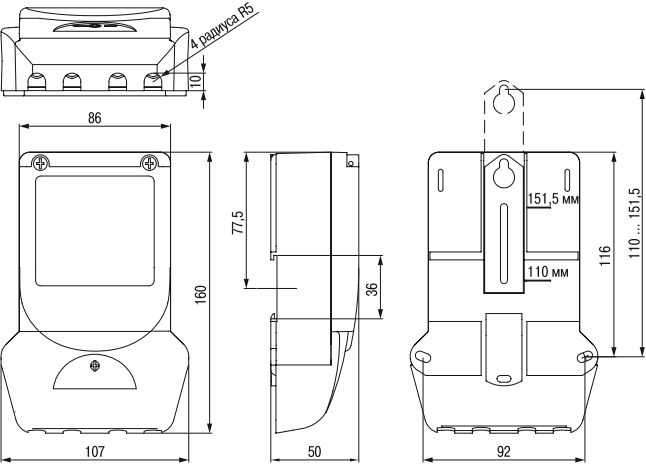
Габаритные и присоединительные размеры счётчиков габарита корпуса 4
